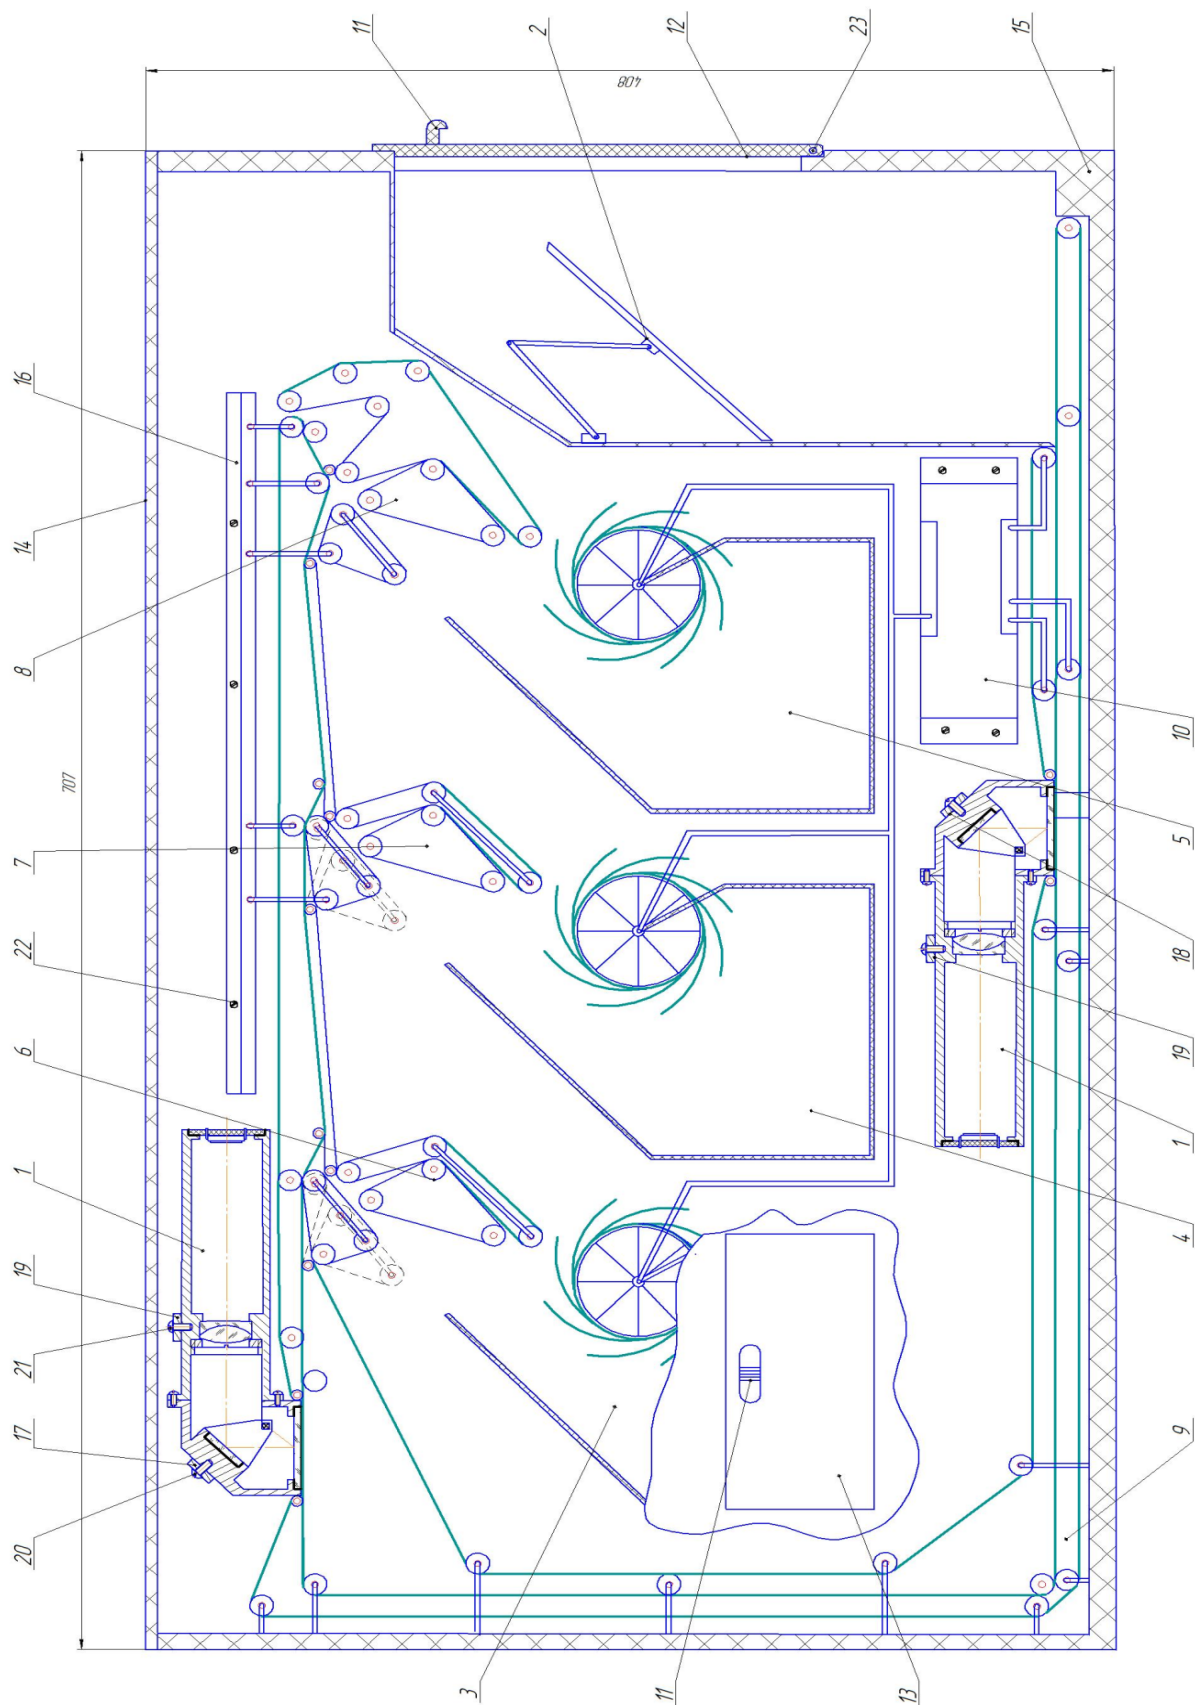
Загальна схема приладу. 1-оптичний блок; 2-фіксатор; 3,4,5-відсіки для відсортованих купюр; 6,7,8-вузли сортування; 9-транспортна стрічка; 10-блок двигуна; 11-ручка; 12-кришка приймального блоку; 13-кришка першого відсіку; 14-кришка корпусу; 15-корпус; 16-кронштейн; 17,18,19-планка; 20,21,22,23-гвинт.
